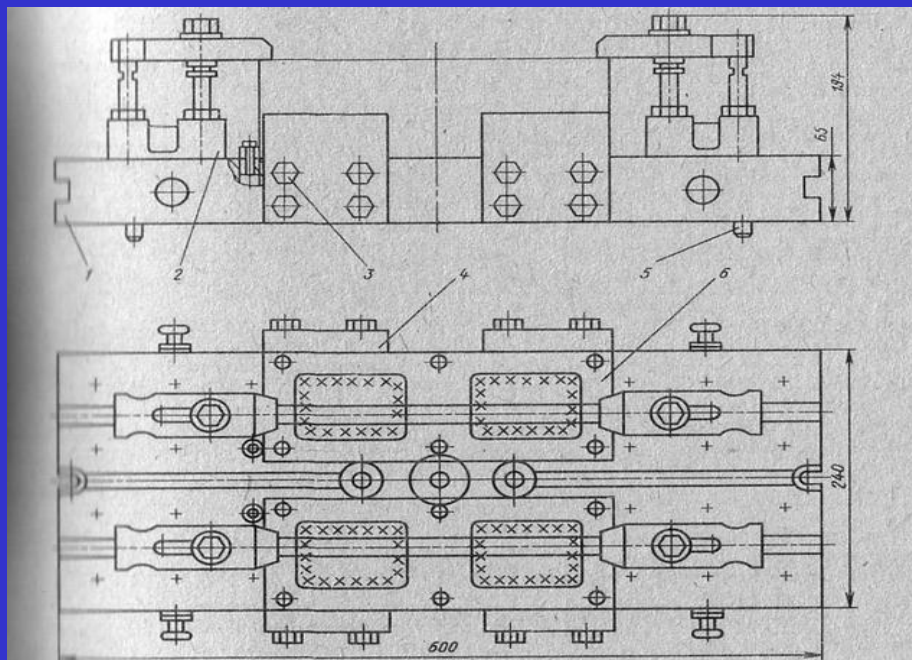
Сборно-разборное приспособление для установки заготовок деталей типа корпуса при сверлении и фрезеровании:
